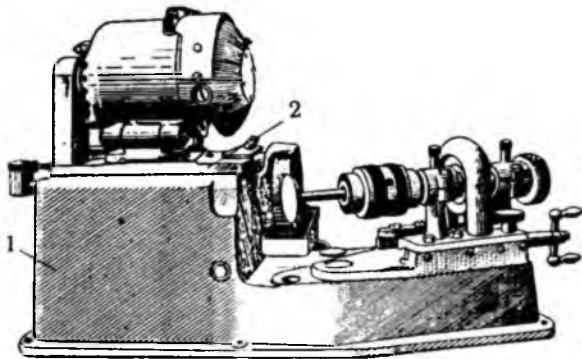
Прибор для шлифовки фасок клапанов с электромотором:
